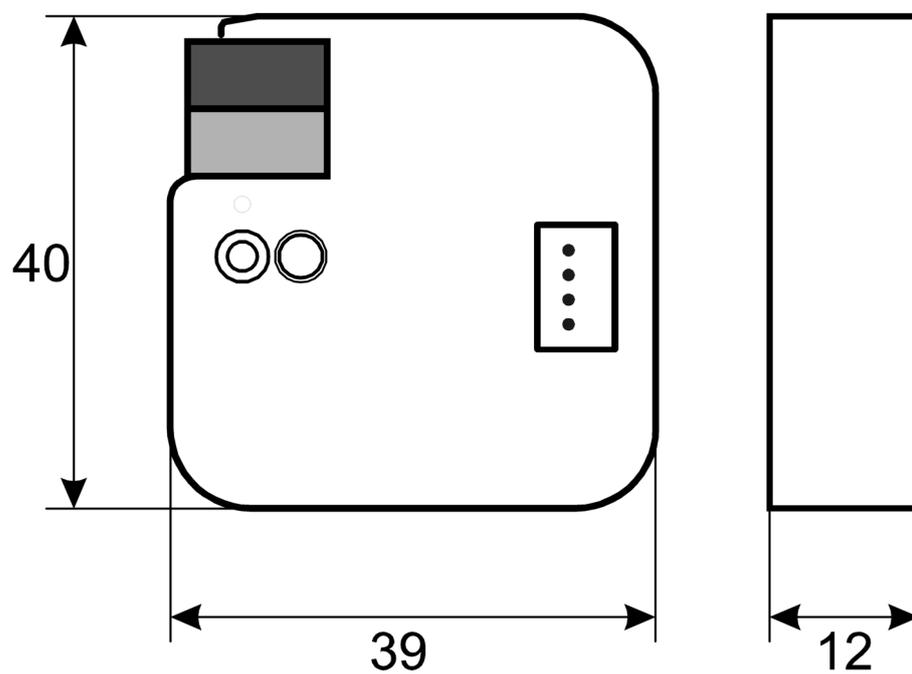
Dimensions de la passerelle Split Unit Gateway (cotes en mm)
